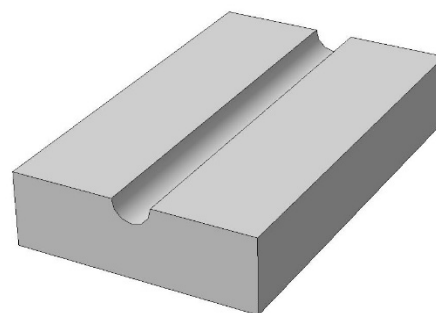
Оснащення для шліфування бічної поверхні багатогранної заготовки.
